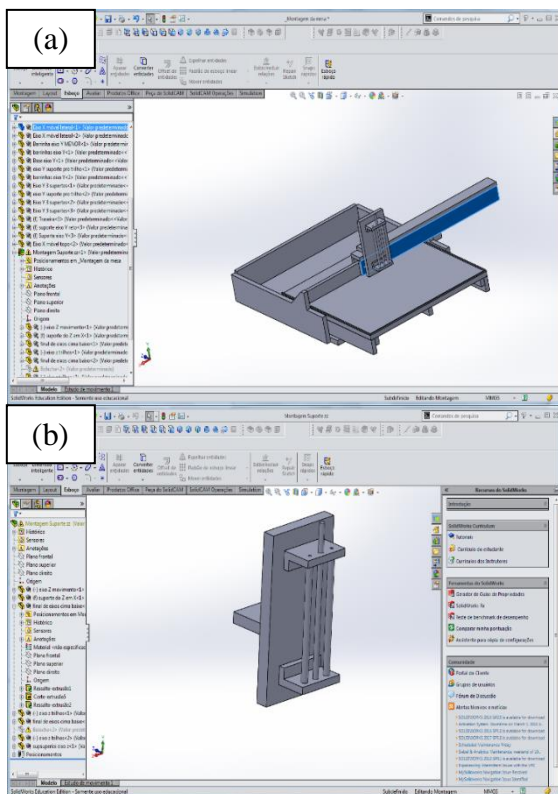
(a) Montagem CAD do protótipo finalizado (b) Montagem CAD do terceiro eixo
